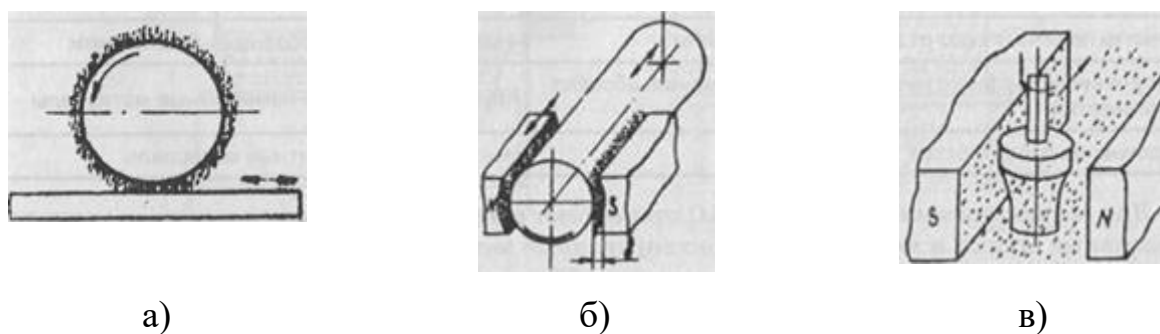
Схеми МАО з розміщенням магнітно-абразивного порошку: а) - на активній поверхні; б) - в робочих зазорах; в) - в робочій зоні
